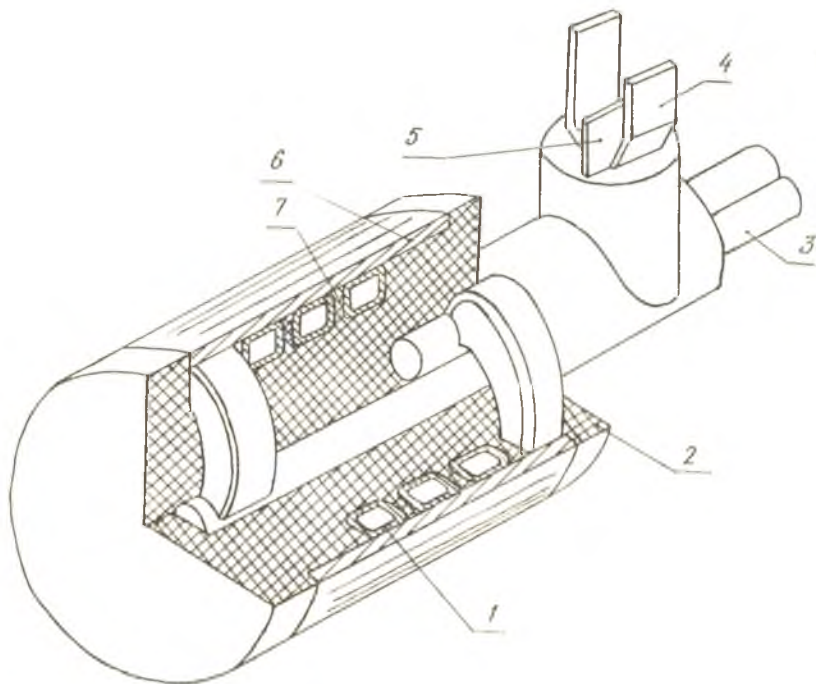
Многовитковый индуктор для раздачи трубчатых заготовок с системой охлаждения: 1 — токопровод, 2 — основание, 3 — штуцер охлаждения, 4 — токоподвод, 5 — прокладка, 6 — главная изоляция, 7 — витковая изоляция
